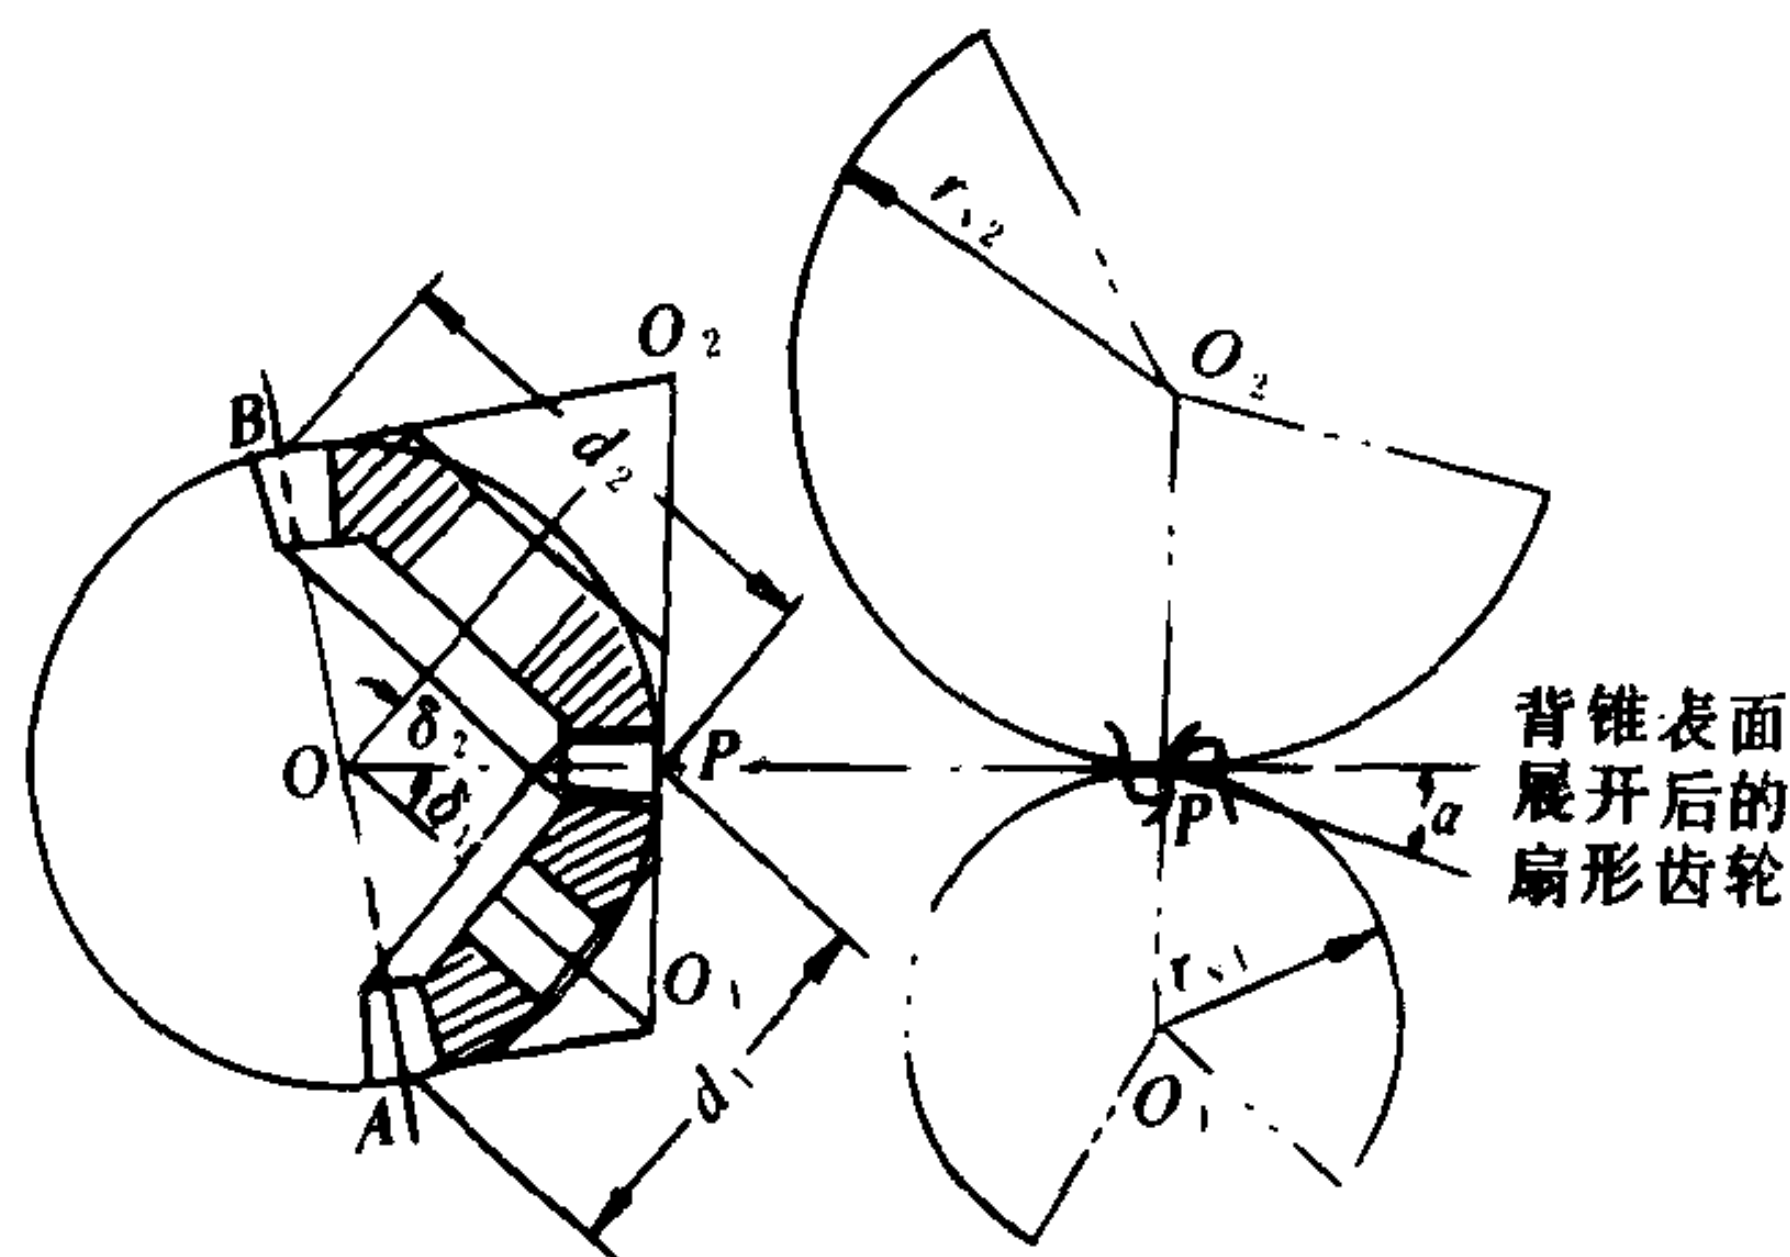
圆锥齿轮的当量圆柱齿轮
